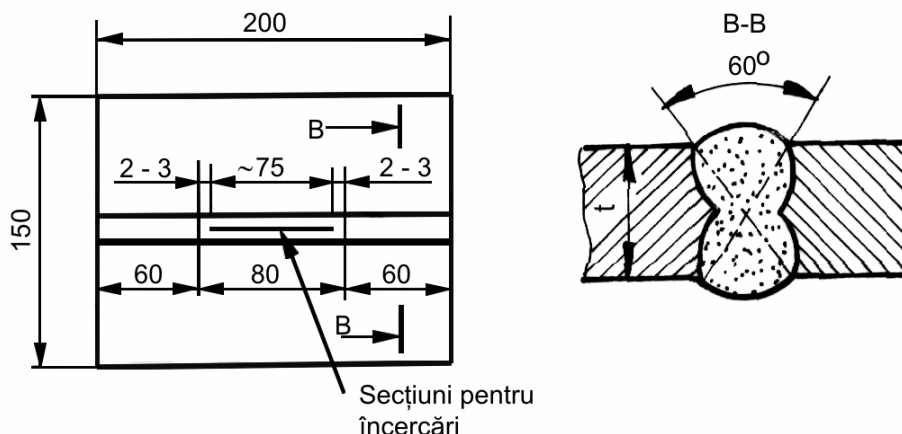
Dimensiunile epruvetei tip Tekken modificată
